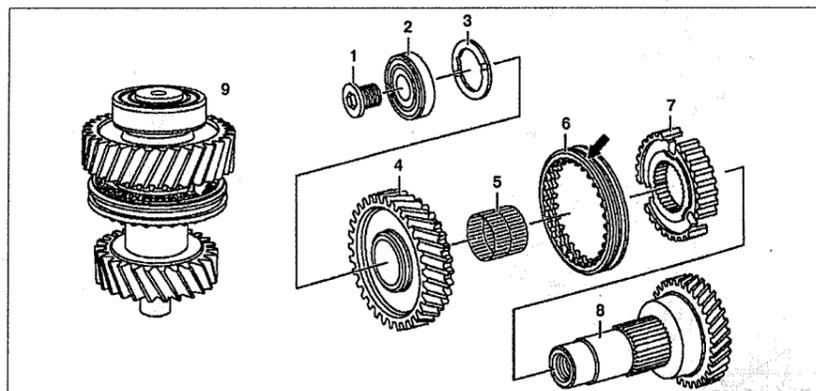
Вал передачи заднего хода (автомобили с двигателями 611.980):
